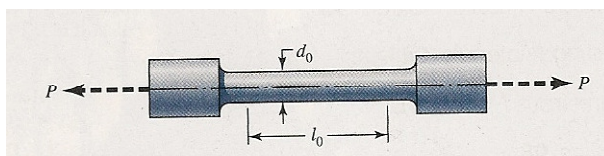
Um corpo-de-prova de ensaio de tração típico (SHIGLEY, 2004).
